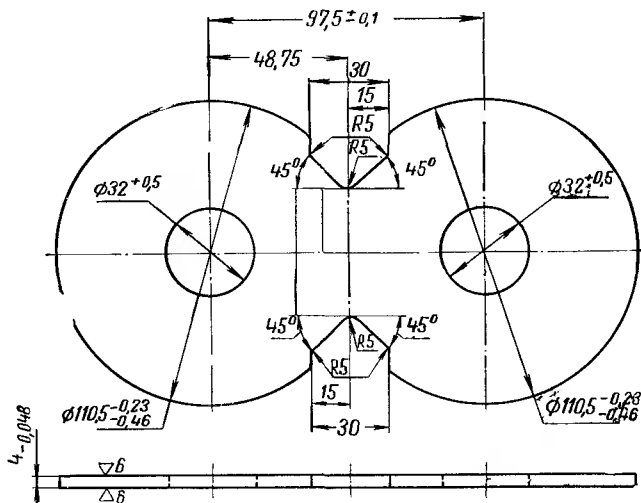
Прокладка шестерни (220В-8604074) масляного насоса подъемного механизма
